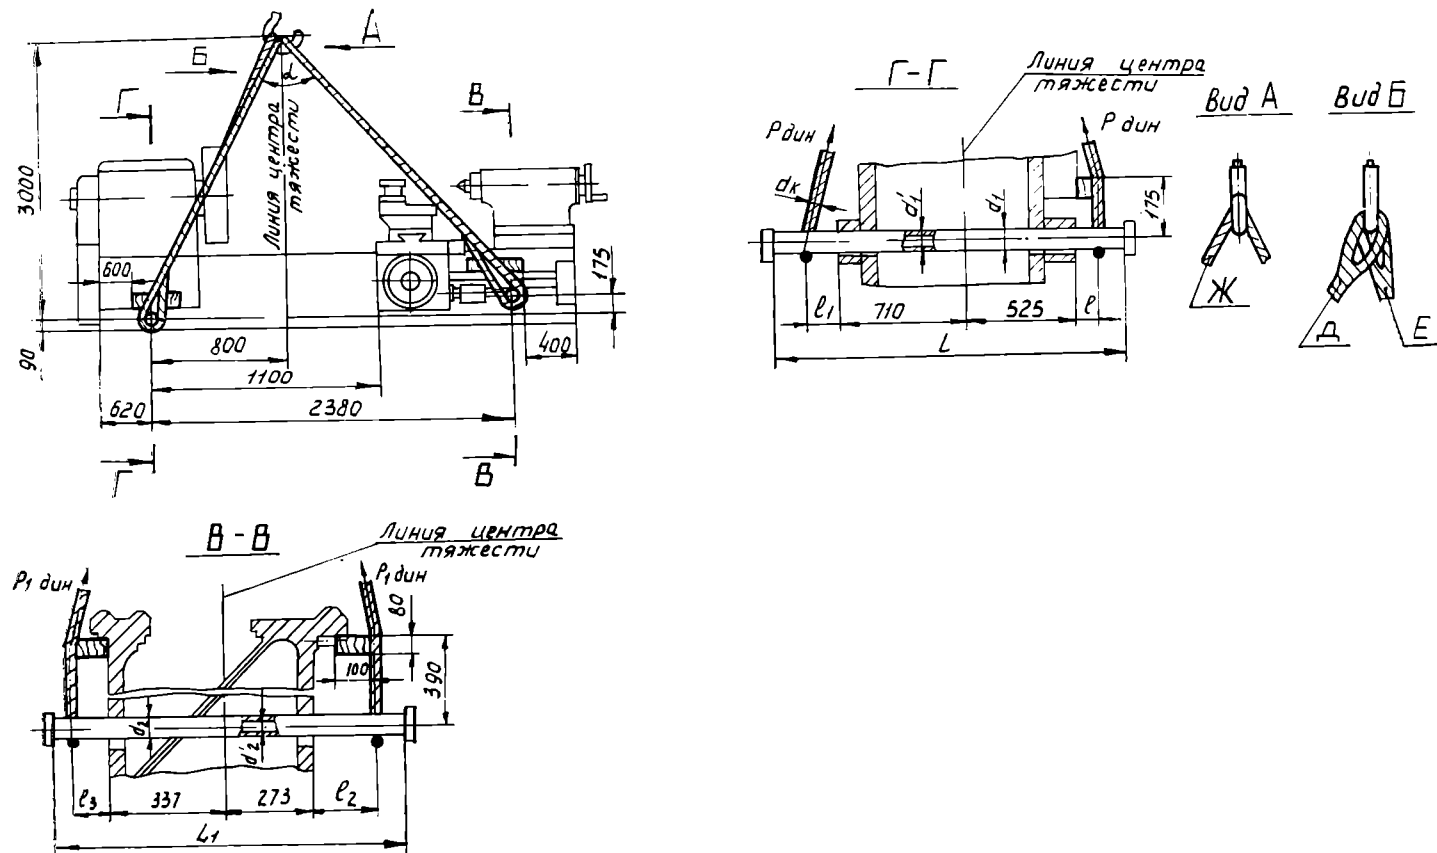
Схема строповки станков мод. ~~ИНС-0~~, ИН65Ф1-0, ИНСГ-1, ИНС-1
